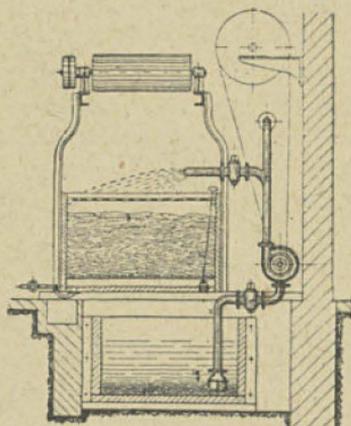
Coupe d'une installation de blanchiment à circulation de liquides.
